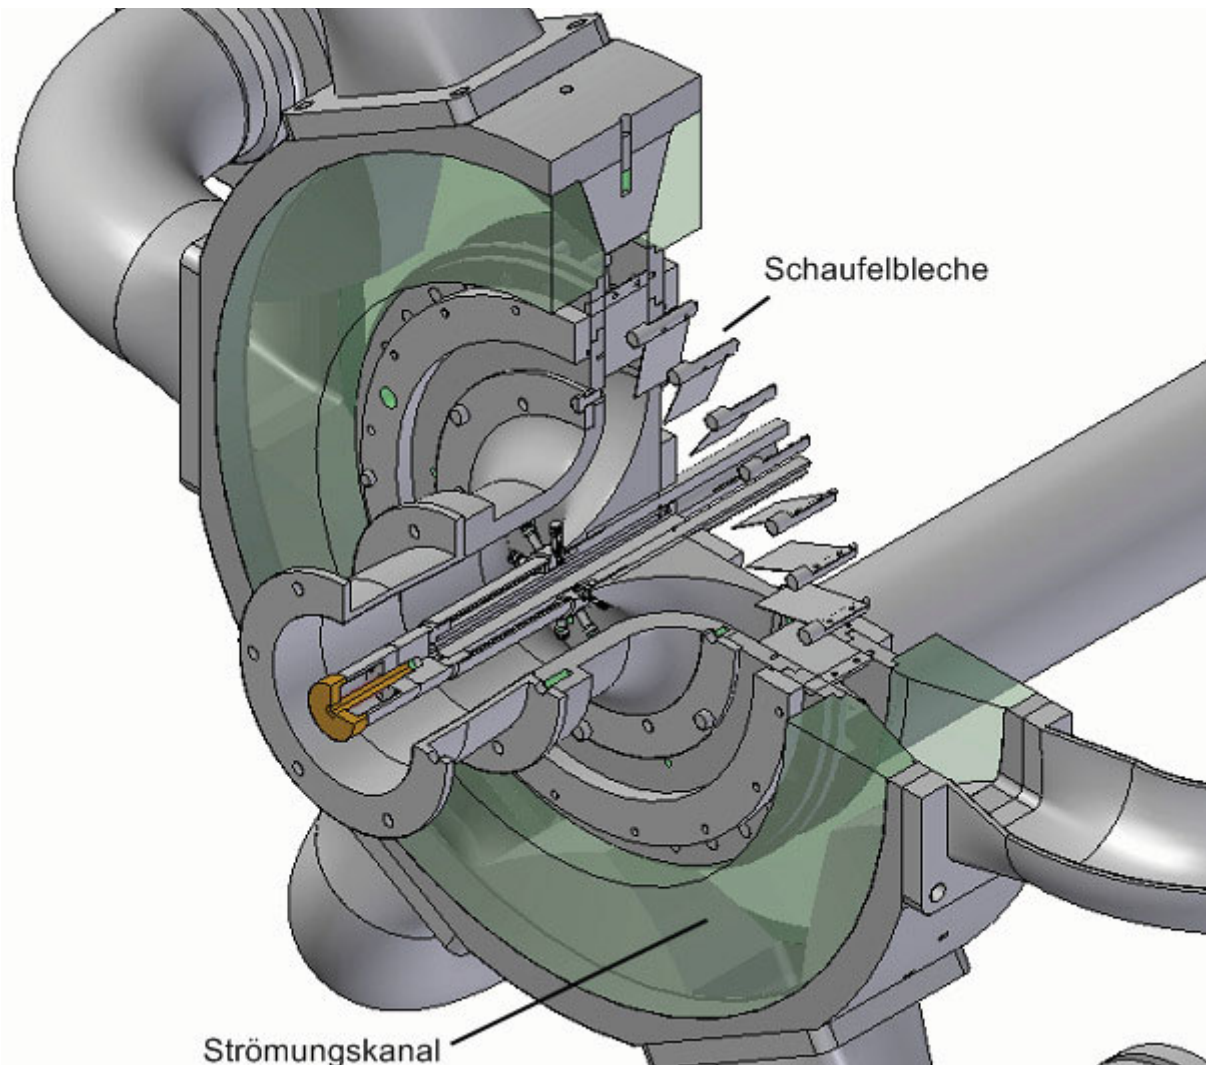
Detailansicht Drallerzeuger (Kaltversuch)
